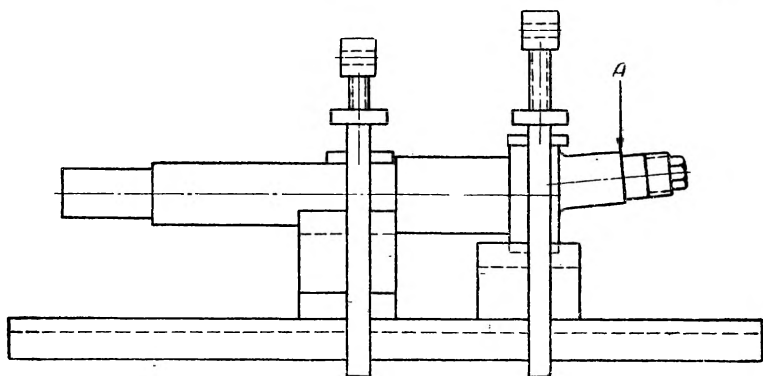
Схема проверки эксцентриковой шейки эксцентрикового вала.
